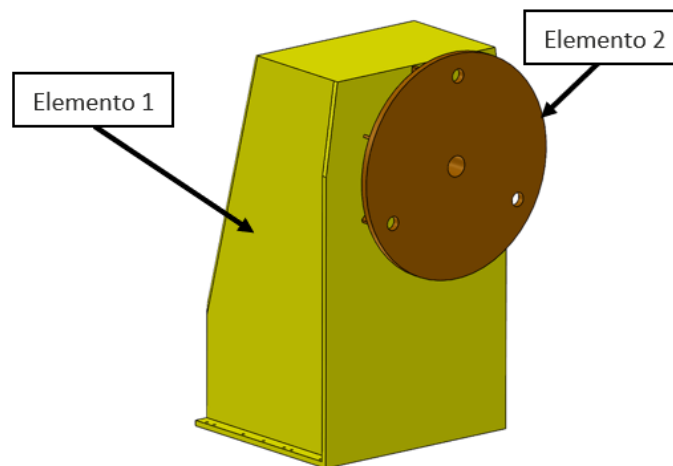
Representação CAD da estrutura da bucha fixadora existente em chão de fábrica: (1) estrutura da bucha e (2) adaptador do prato da bucha fixadora
